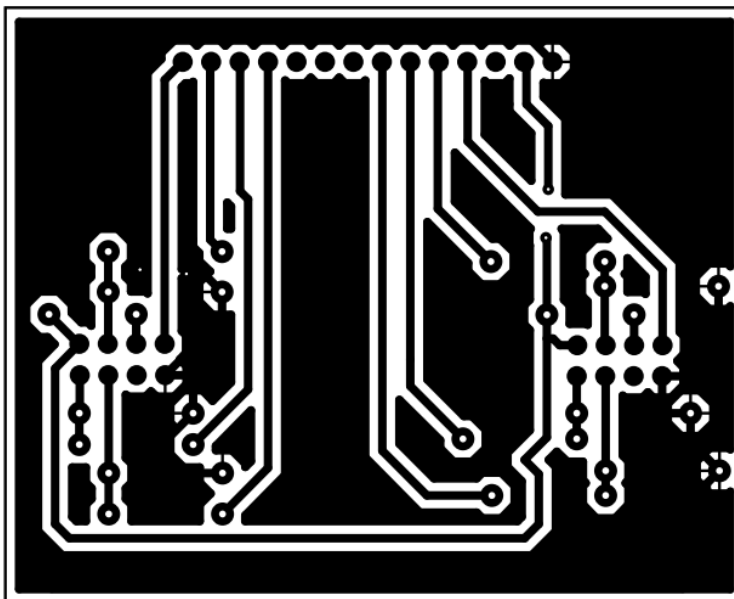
Plantilla PCB para la placa de prueba 1.
